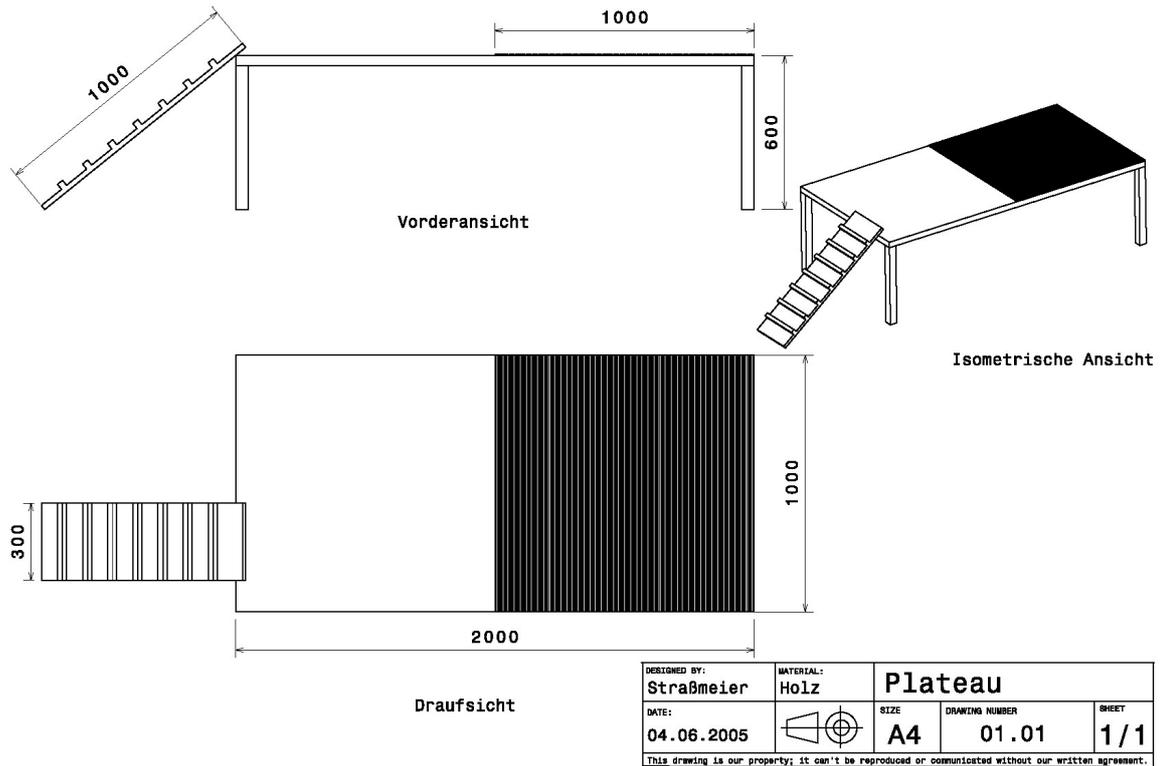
Bauplan eines Plateaus (mit Maßangaben in mm)
